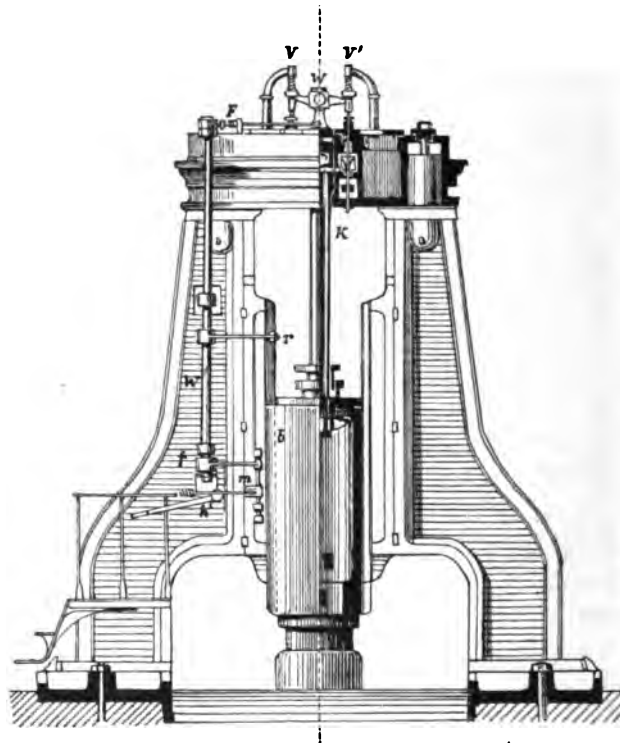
Condiéhammer mit Haswell's Ventilsteuerung.
